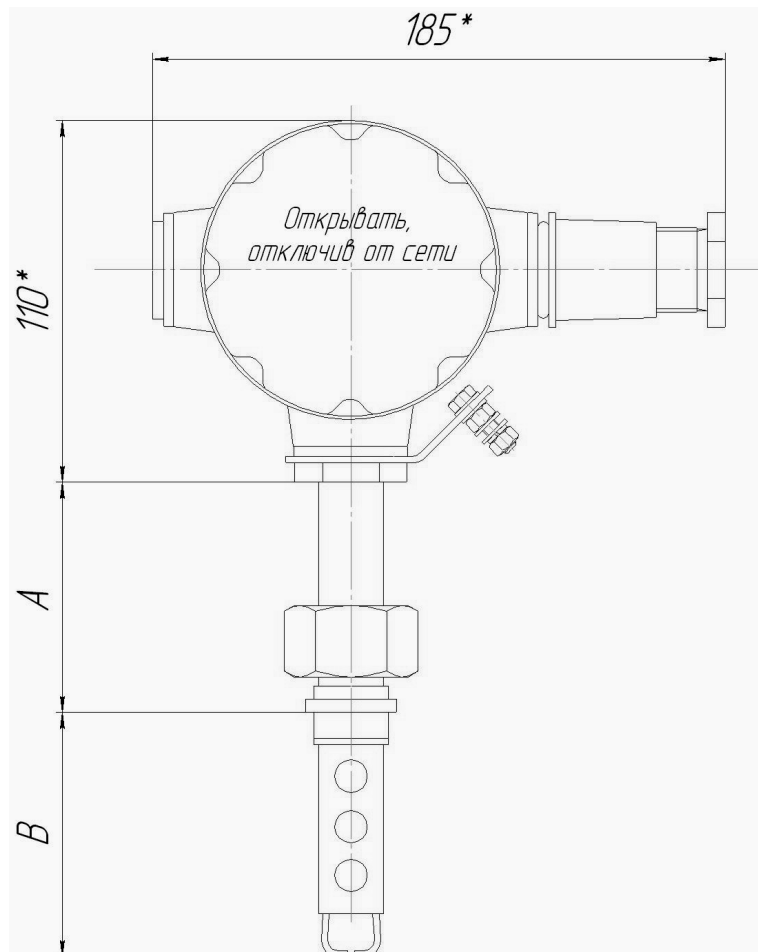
Внешний вид прибора СЖУ-1-ОГ.
